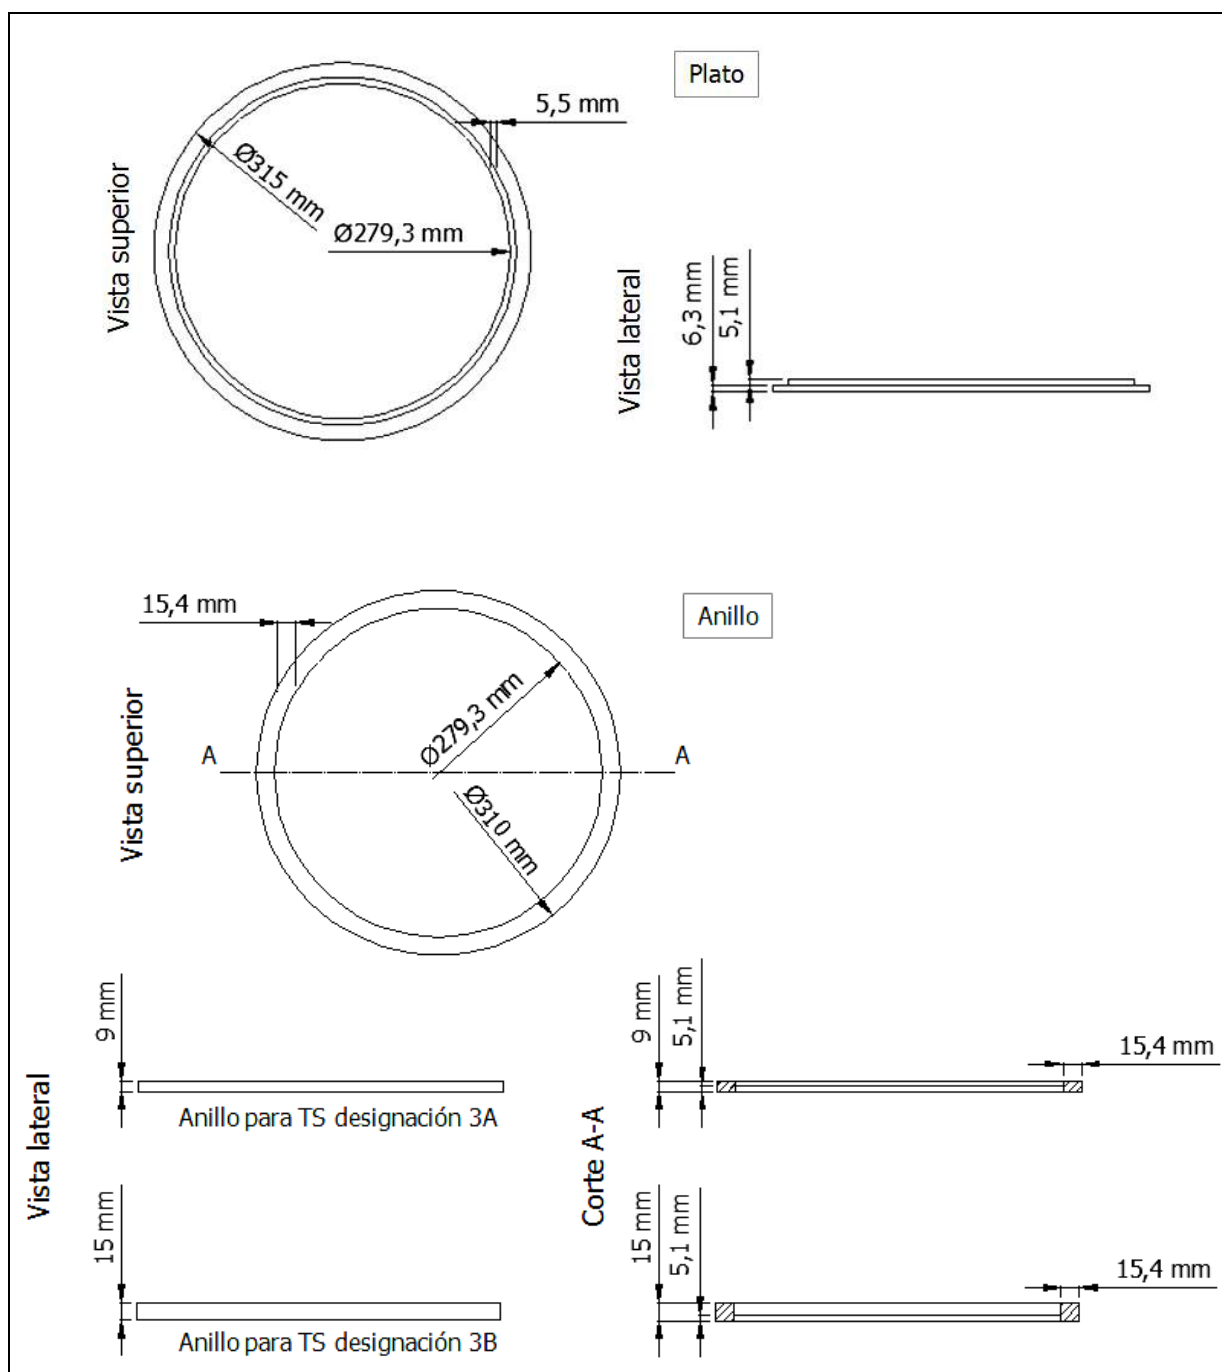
Dimensiones de los moldes para el ensayo de pérdida
